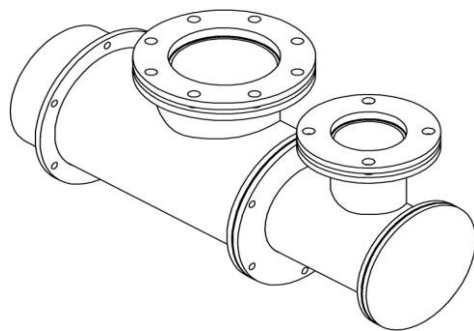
Горелочное устройство ГГВ-150. Внешний вид
